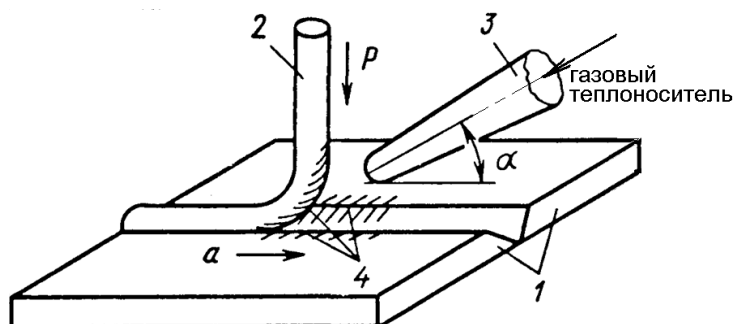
Схема сварки газовым теплоносителем с присадкой:
